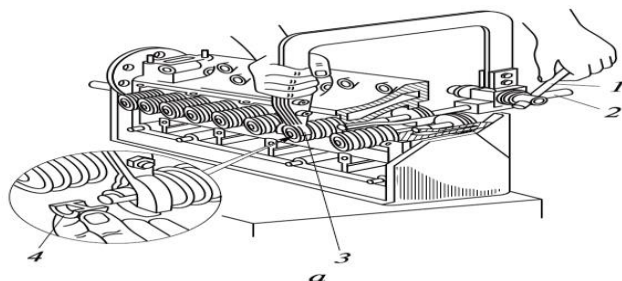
Газораспределительный механизм двигателя ЗМЗ-511.10
